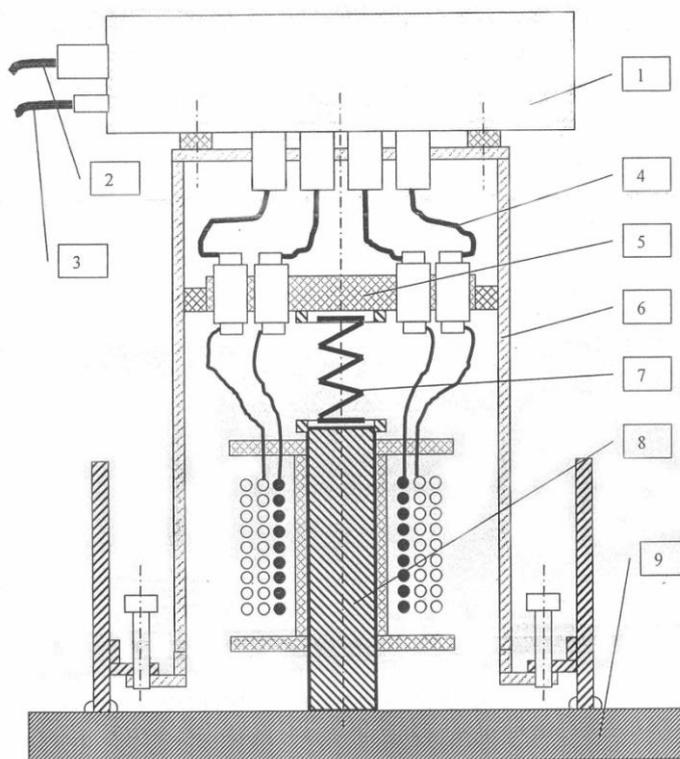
Принципиальная схема электромагнитного излучателя: 1 — силовая разрядная часть; 2 — силовой кабель; 3 — управляющий коаксиальный кабель; 4 — провод; 5 — изолятор; 6 — корпус; 7 — упорная пружина; 8 — сердечник из пакета пластин; 9 — стальной лист стенки бункера
